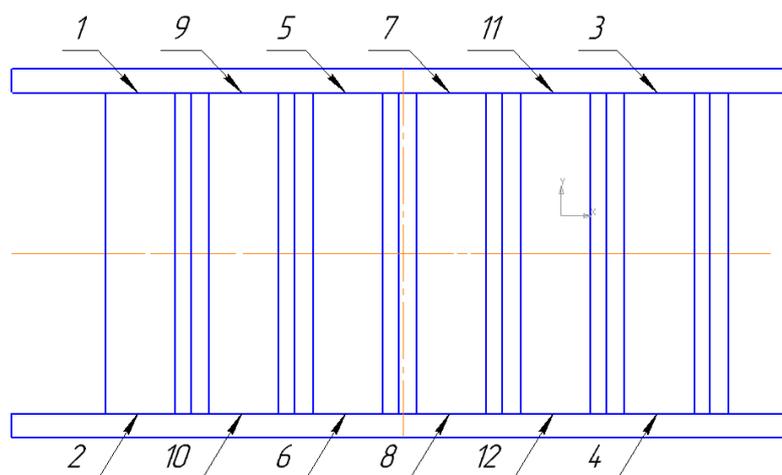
Последовательность сварки лестничного марша
